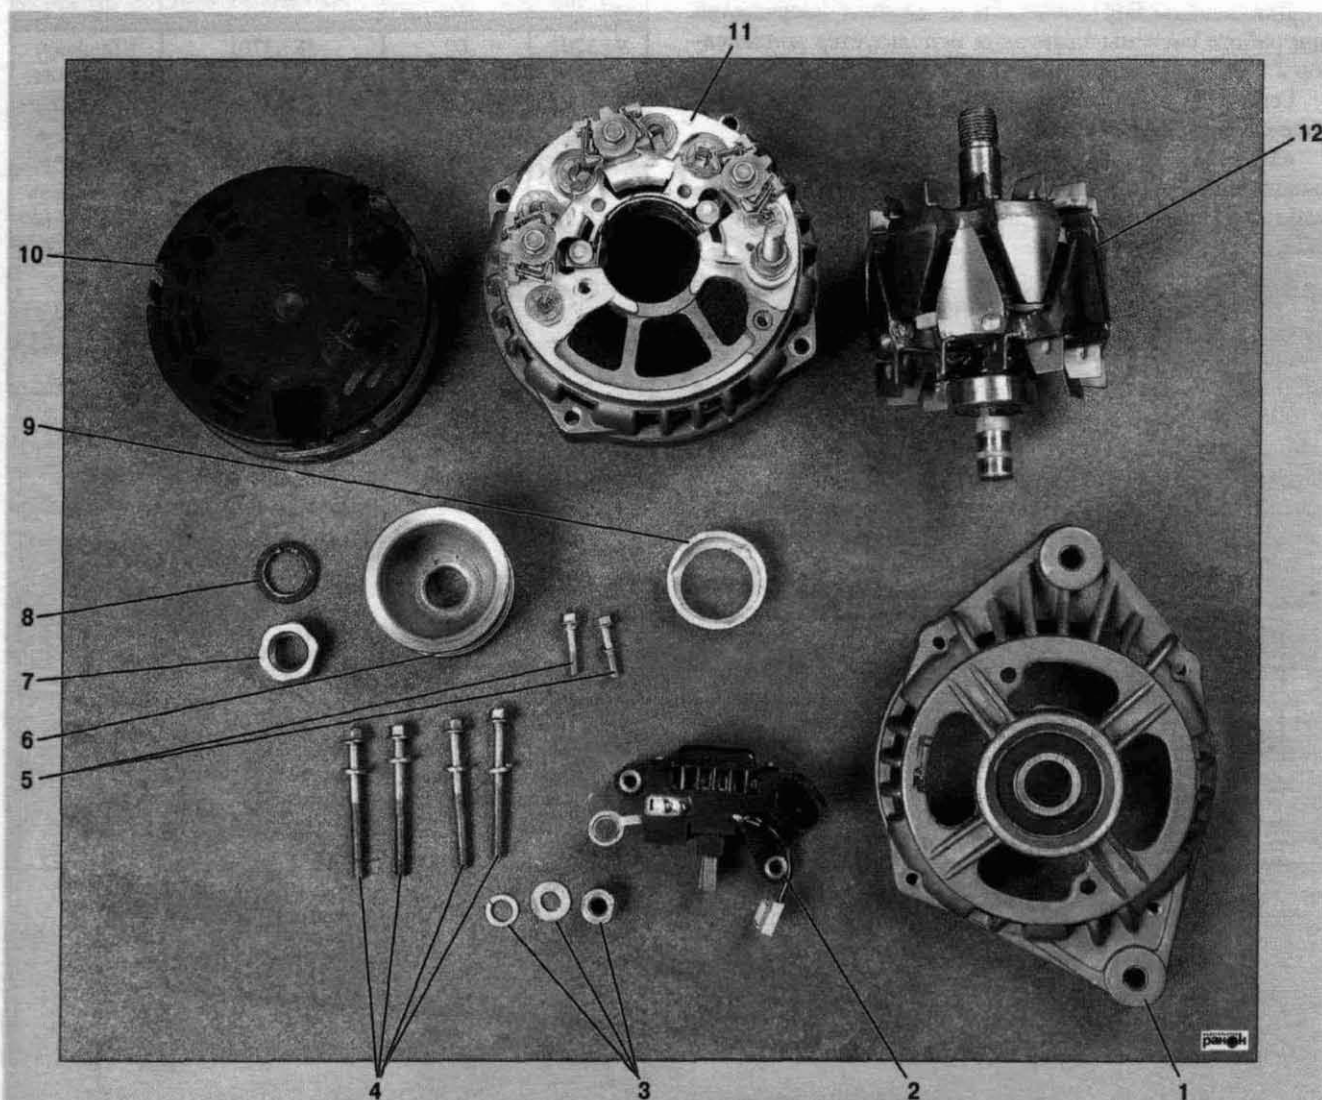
Детали генератора 97.3701: 1 – задняя крышка в сборе с подшипником; 2 – щеточный узел в сборе с регулятором напряжения и конденсатором; 3 – гайка и шайбы крепления регулятора напряжения; 4 – стягивающие болты крышек генератора; 5 – болты крепления регулятора напряжения; 6 – шкив генератора; 7 – гайка крепления шкива; 8 – шайба гайки крепления шкива; 9 – втулка заднего подшипника; 10 – пластмассовая крышка генератора; 11 – передняя крышка генератора в сборе с выпрямительным блоком и статором; 12 – ротор генератора в сборе с передним подшипником
